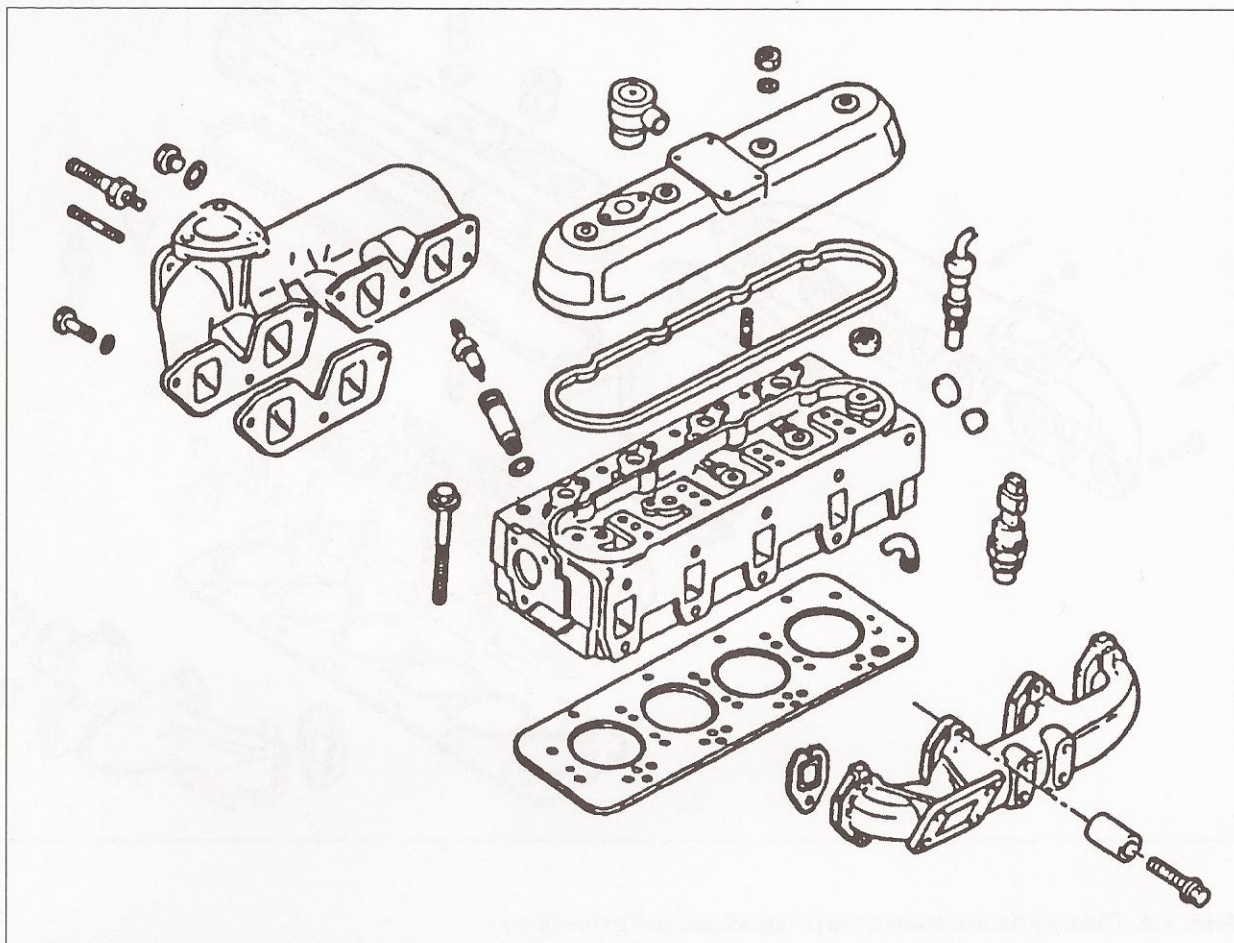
Головка блока цилиндров (4-цилиндровый двигатель).
